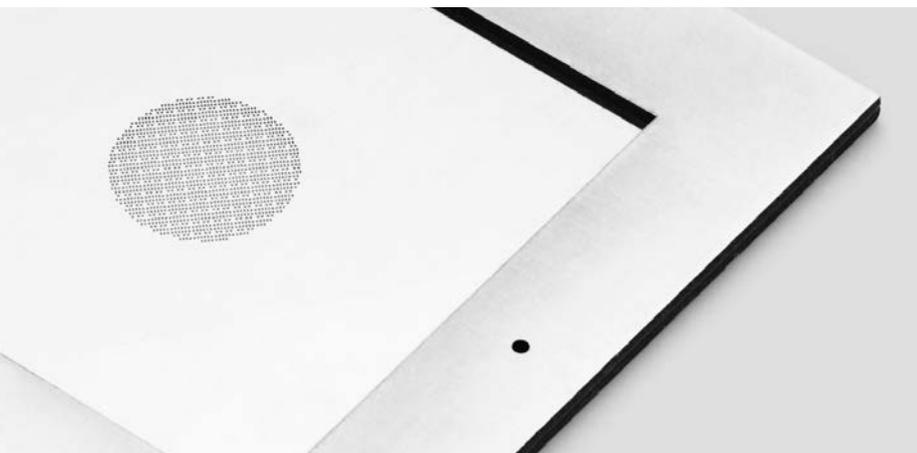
Rahmen als Trägerplatte verschweißt
